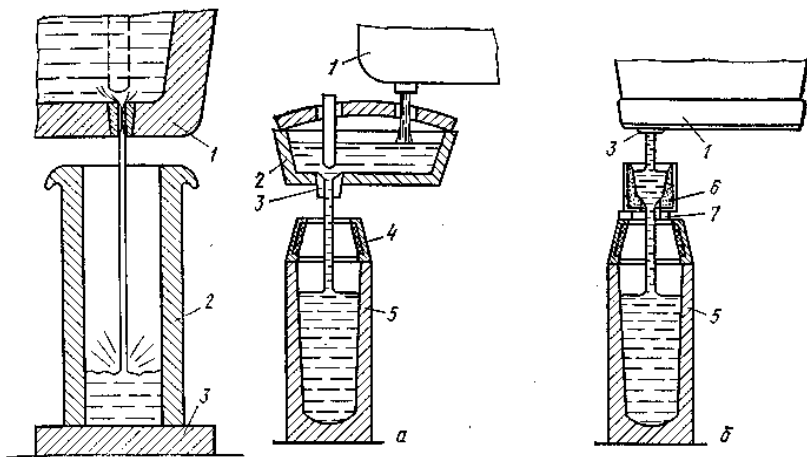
Схема разливки стали сверху, через промежуточный ковш (а) и промежуточную воронку (б)
